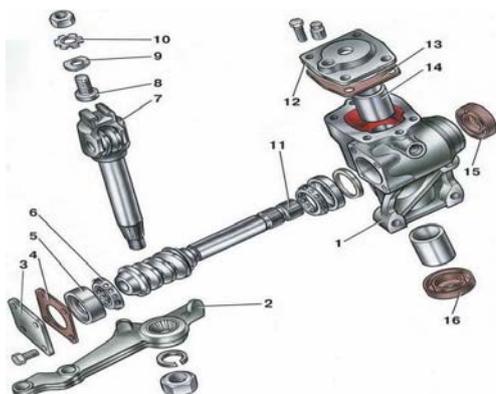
Рулевой редуктор ВАЗ-2107
